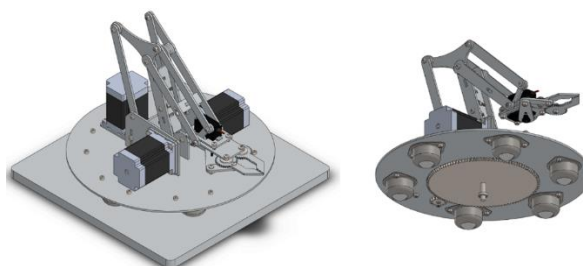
Vista isométrica e inferior del diseño 3D de la versión final
